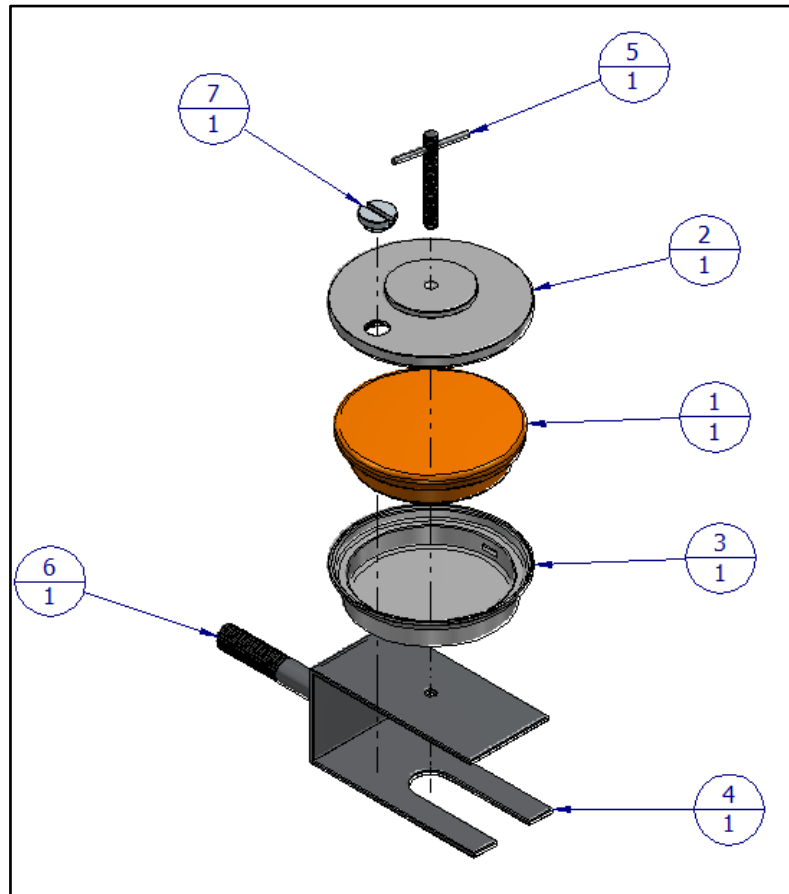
Despiece molde de Rotomoldeo para pieza Prototipo.
